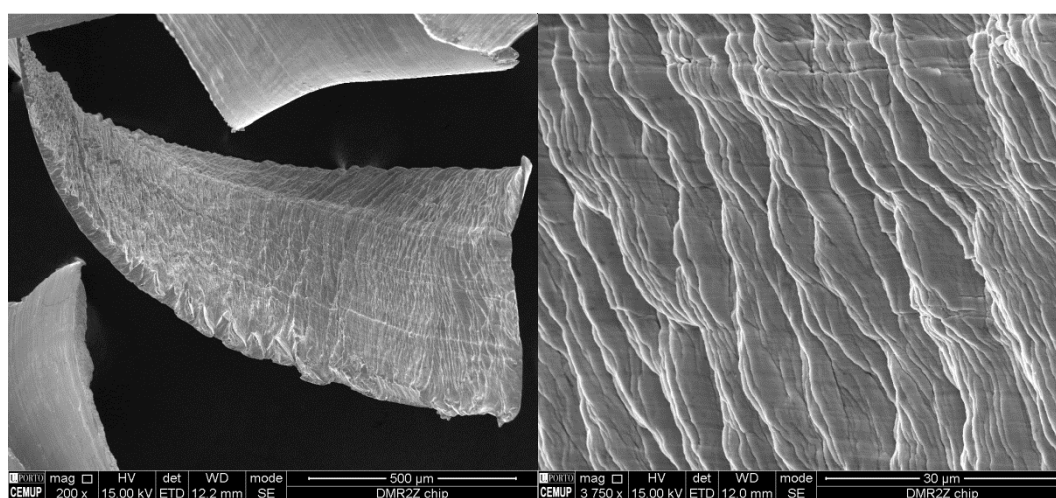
Apara da DORMER 2Z em 8 ciclos e pormenor da face de esmagamento
